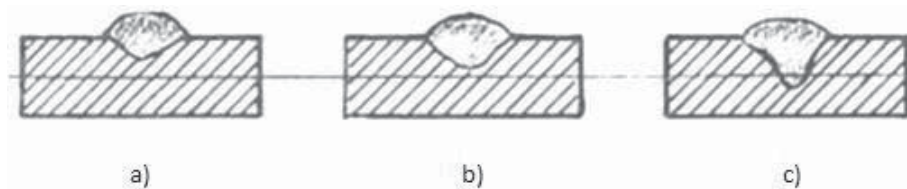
Efecto de diferentes amperajes en el cordón de soldadura, a) 100A, b) 150 A y c) 200 A.
